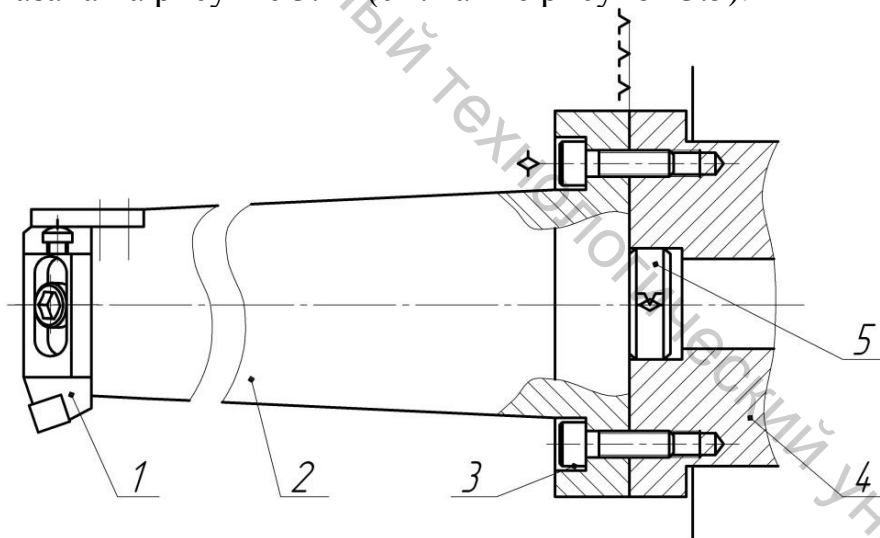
Крепление борштанги с резцовой вставкой в шпинделе горизонтального алмазно-расточного станка: 1 – резцовая вставка; 2 – борштанга; 3 – винты крепления; 4 – шпindel расточной бабки; 5 – центрирующий пояс борштанги
